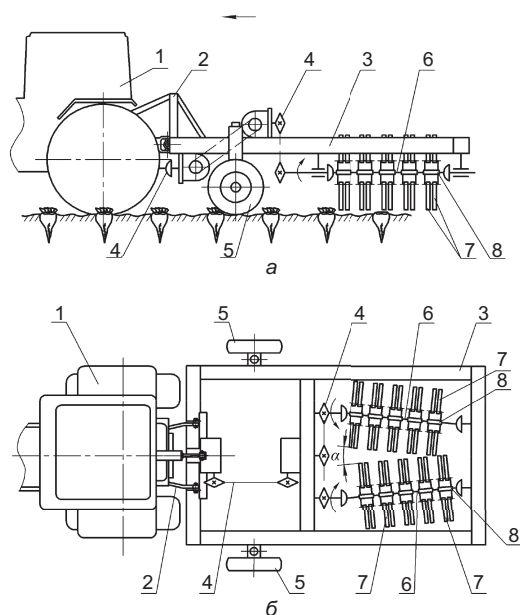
Конструктивна схема очисника: а — вигляд збоку; б — вигляд зверху; 1 — трактор; 2 — зчіпка; 3 — основна рама; 4 — елементи приводу; 5 — копіювальні колеса; 6 — приводні вали; 7 — робочі органи; 8 — обойми
